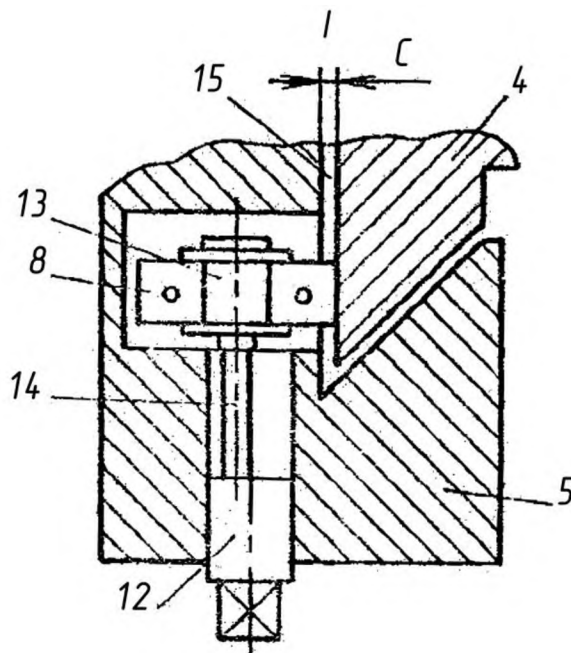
Вузол I радіально-свердлильного верстата
